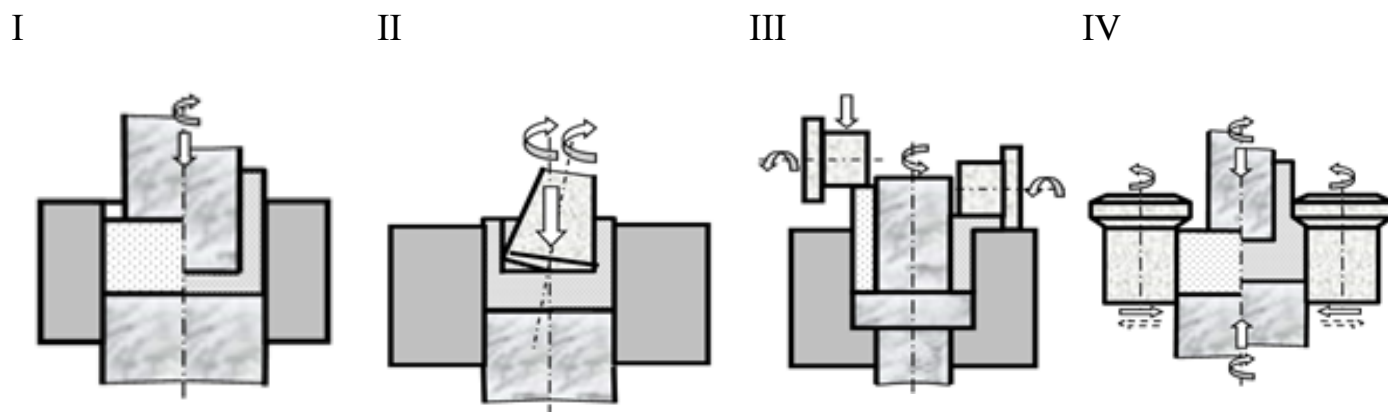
Способи виготовлення порожнистих деталей із суцільних та трубчастих заготовок із різною кінематикою руху інструменту
